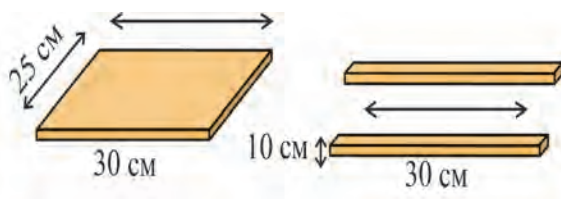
Разметка при изготовлении шкатулки и заготовка ноготковых соединений:
